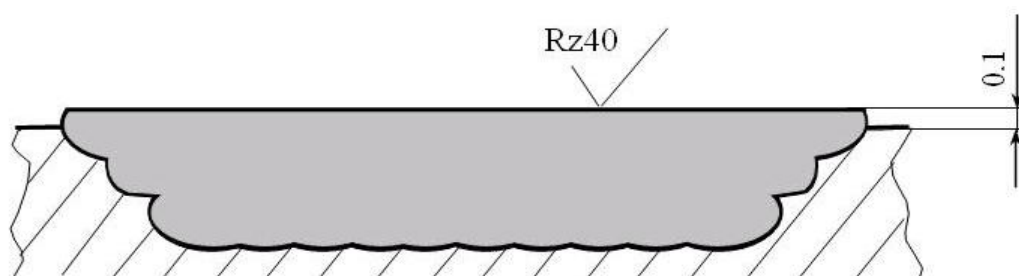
Геометрические параметры сварного шва наложенного на место выборки и после поверхностной механической обработки
